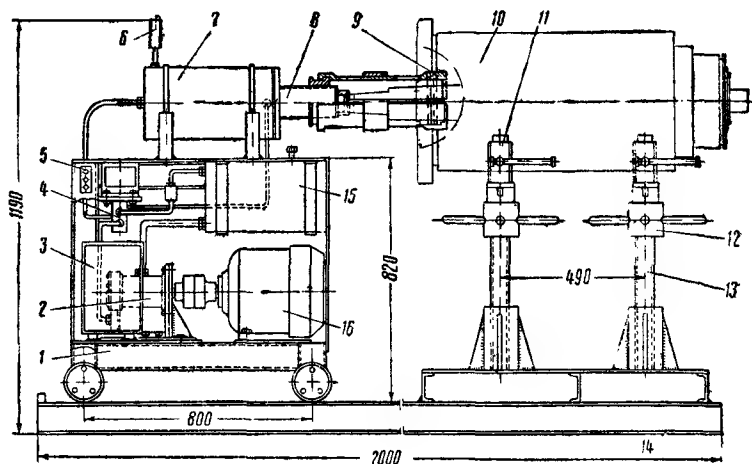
Горизонтальный гидравлический пресс для снятия упорных и лабиринтовых втулок с вала якоря:
